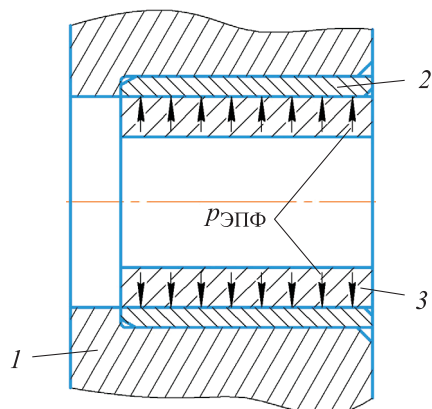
Схема процесса получения ССН деталей типа «втулка — корпус» с использованием ЭПФ-привода:
